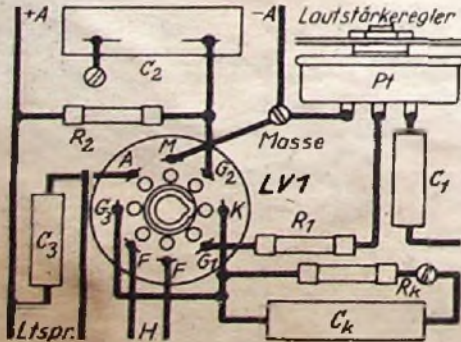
Verdrahtungsplan einer Endstufe mit LV 1
